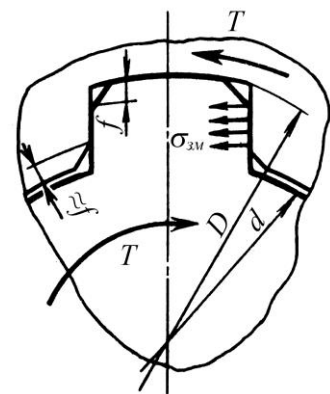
Розрахункова схема шліцьового з'єднання
